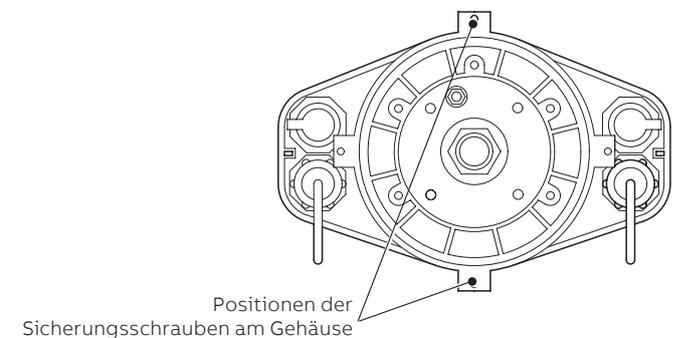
Positionen der Sicherungsschrauben des externen Messumformers (FET432) (Rückansicht)
